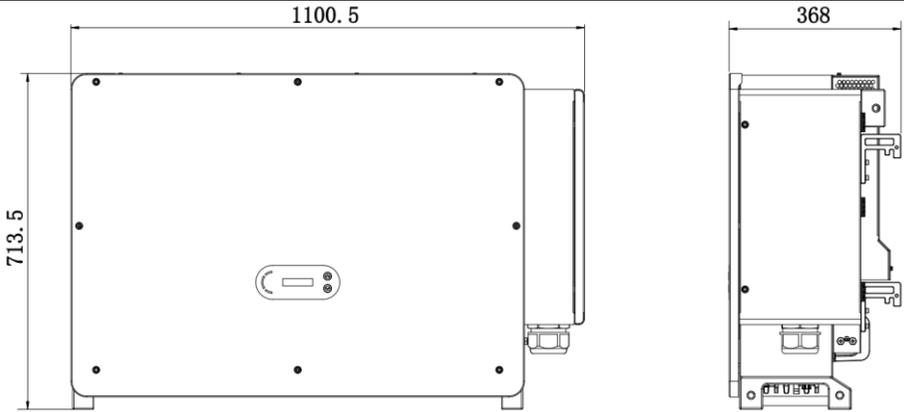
Dimensions de la vue avant et de la vue gauche du produit
